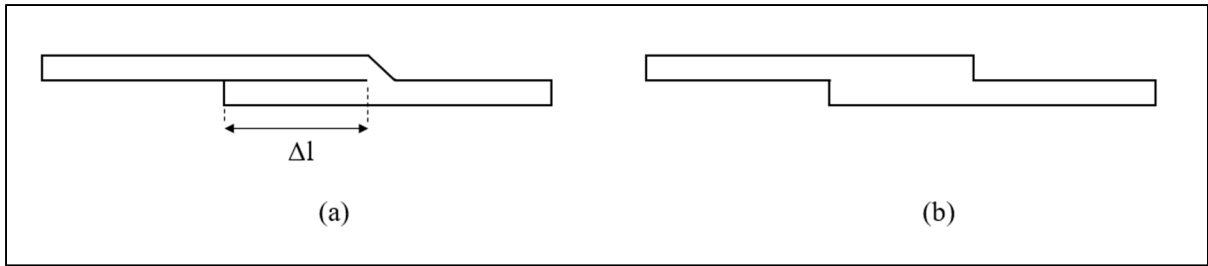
Liaison de deux plaques par (a) joint soudé et (b) joint adhésif ou brasé
